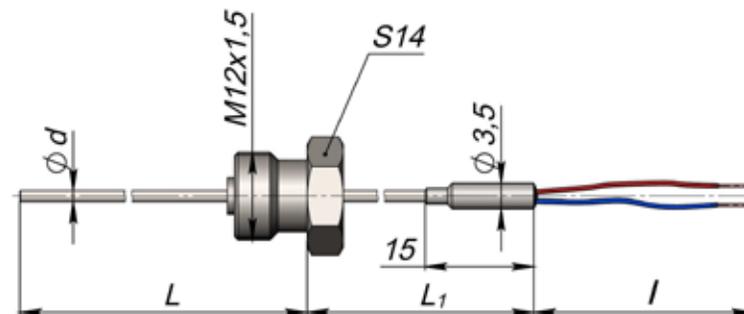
Сборка термопреобразователя с неподвижным штуцером – ШН
